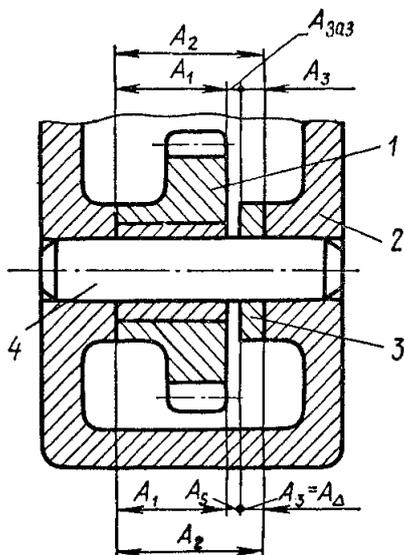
Размерная цепь (фрагмент чертежа редуктора)
